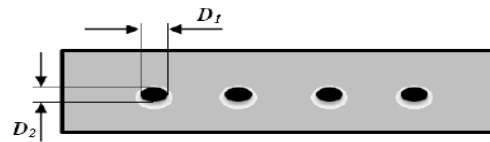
Descripción de la medición de los puntos de soldadura.
